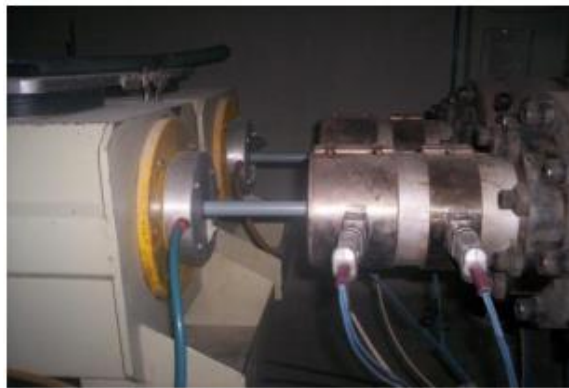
Proceso de Extrusión Fuente: (Mera Rivera, 2014)
